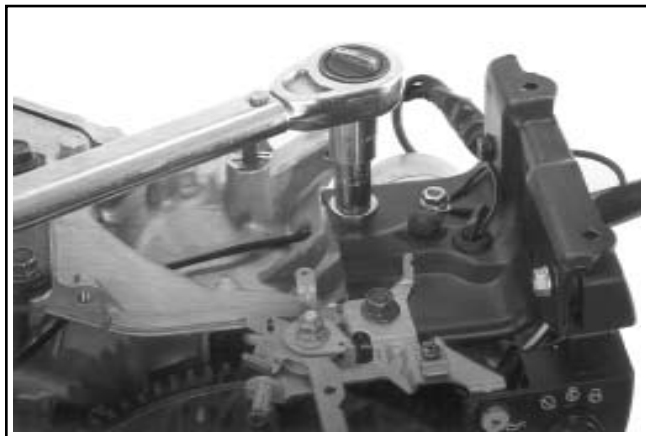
CS8.5 (n° spec. 92xxxx) 10, CS-12. Montaggio del supporto del carburante del combustibile di destra.
